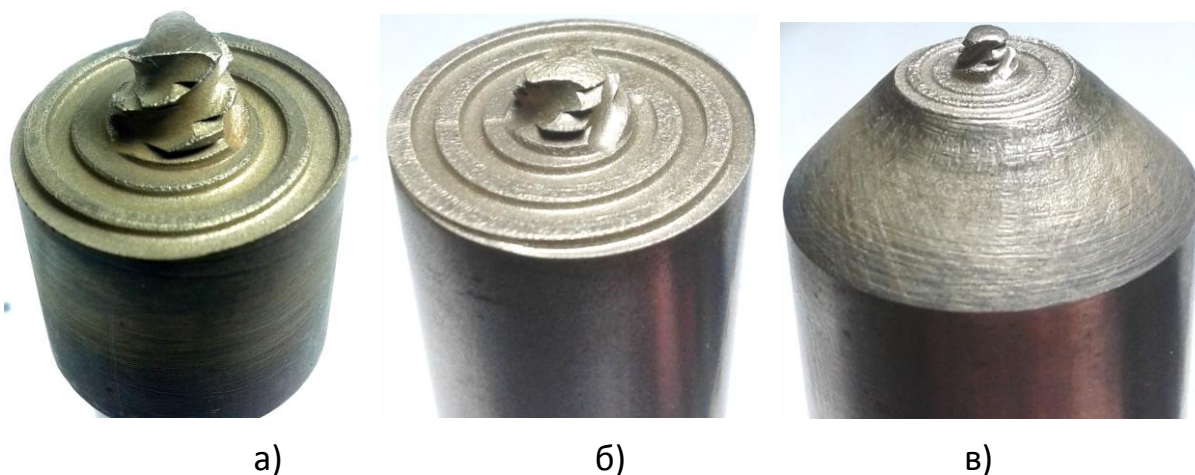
Сложнопрофильный инструмент для сварки трением с перемешиванием, полученный методом ЭЭФ для ПСТ листового материала толщиной соответственно: а – 8 мм; б – 4 мм; в – 2 мм
